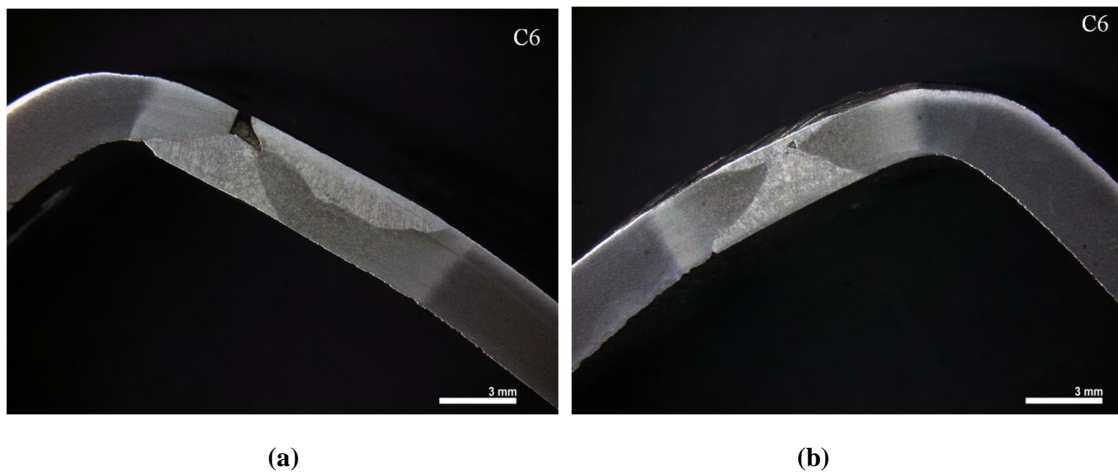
Macrografías de las uniones soldadas del acero C6.
